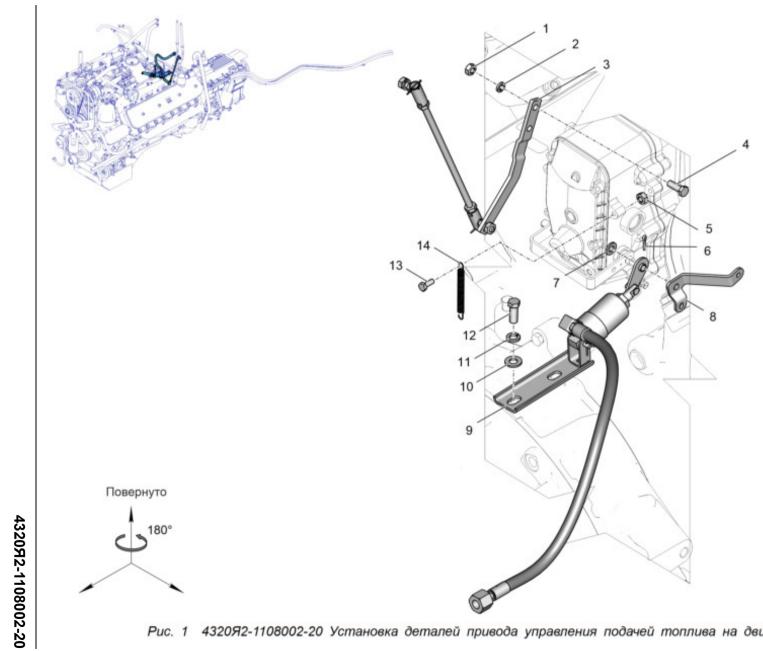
4320Я2-1108002-20 Установка деталей привода управления подачей топлива на двигателе
